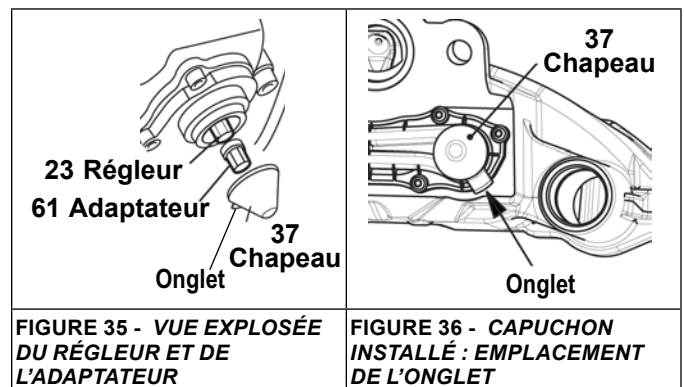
VUE EXPLOSÉE DU RÉGLEUR ET DE L'ADAPTATEUR
